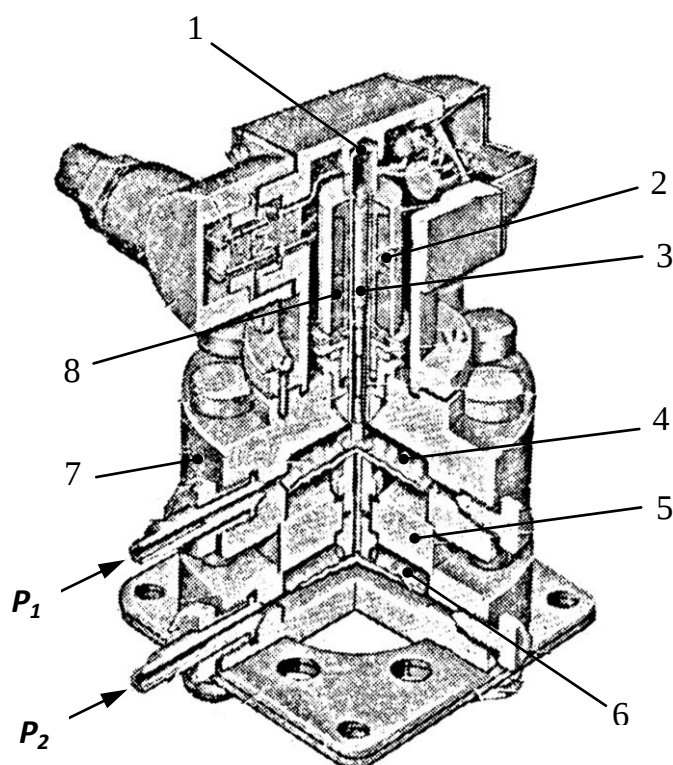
Первичный прибор дифференциального манометра: 1 – разделительная трубка; 2 – катушки; 3 – ферромагнитный сердечник; 4 – верхняя мембранная коробка; 5 – разделительная диафрагма; 6 – мембранная коробка; 7 – корпус; 8 – катушки
